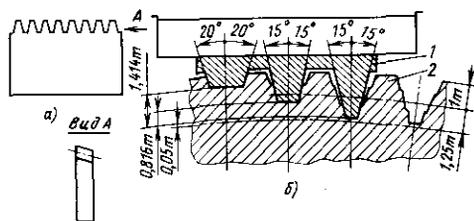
Гребенки зуборезные: а — прямозубая; б — прямозубая с переменной высотой и углом профиля
